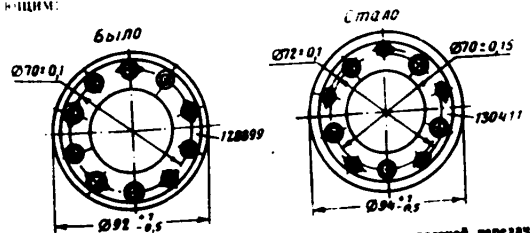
Сателлит валика редуктора двухскоростной передачи магнетала. Фиг. 185. Валик сателлита валика редуктора двухскоростной передачи магнетала.
